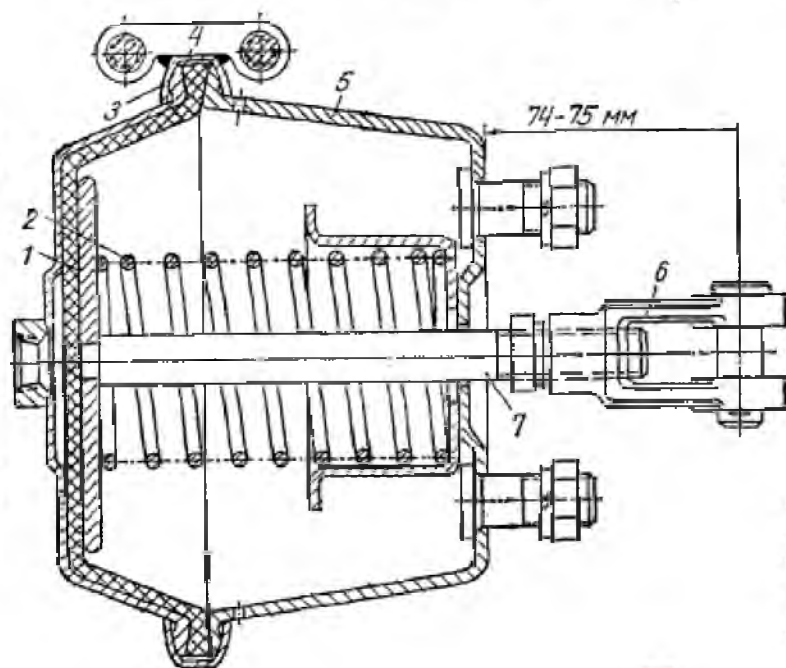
Гальмівна камера: 1 - діафрагма; 2 - пружини; 3 - хомутик; 4 - кришка; 5 - корпус; 6 - вилка; 7 - шток.
